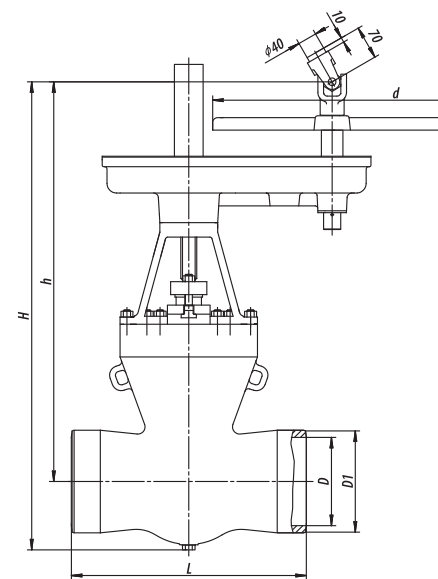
Задвижка DN150...400 с цилиндрическим редуктором
